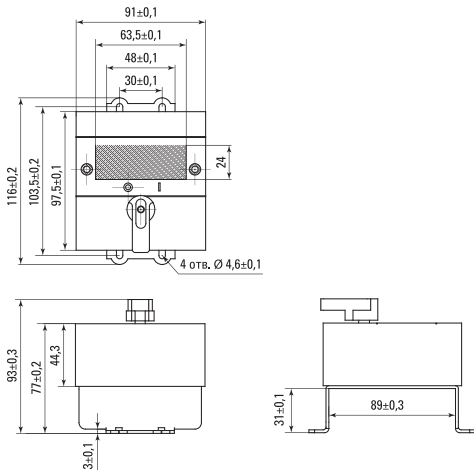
Габаритные размеры моторного привода к ВА-99М 63
